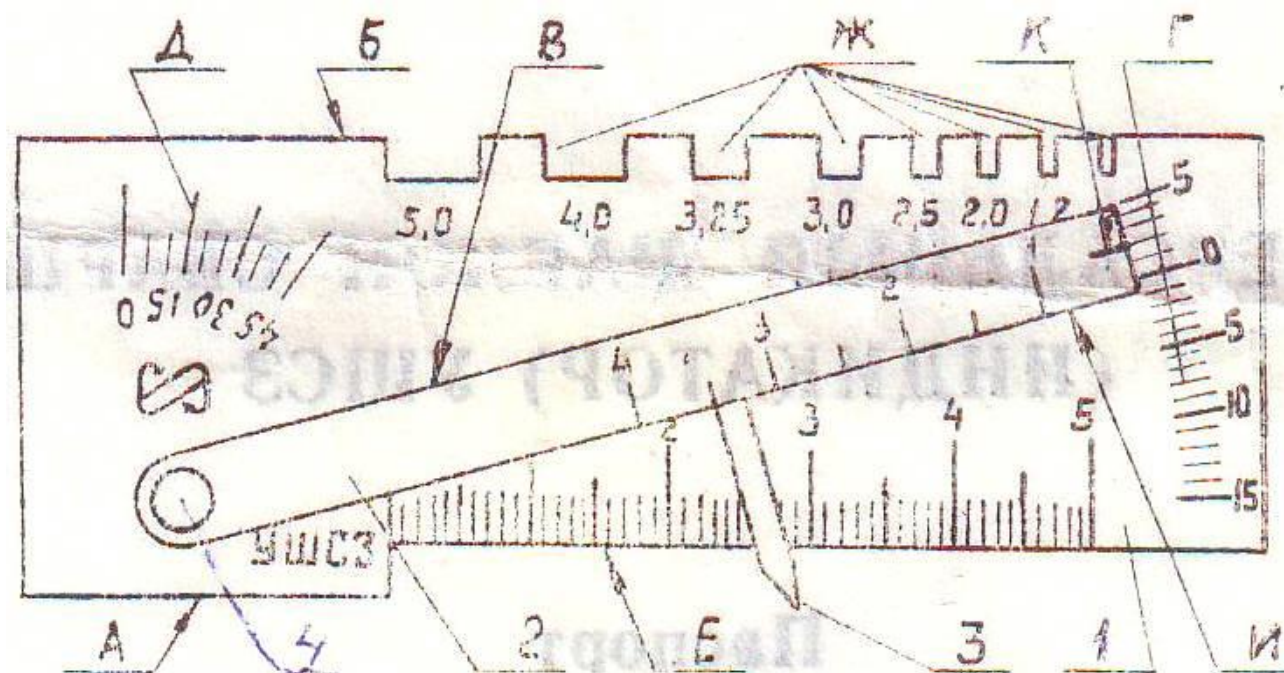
Универсальный шаблон сварщика УШСЗ
